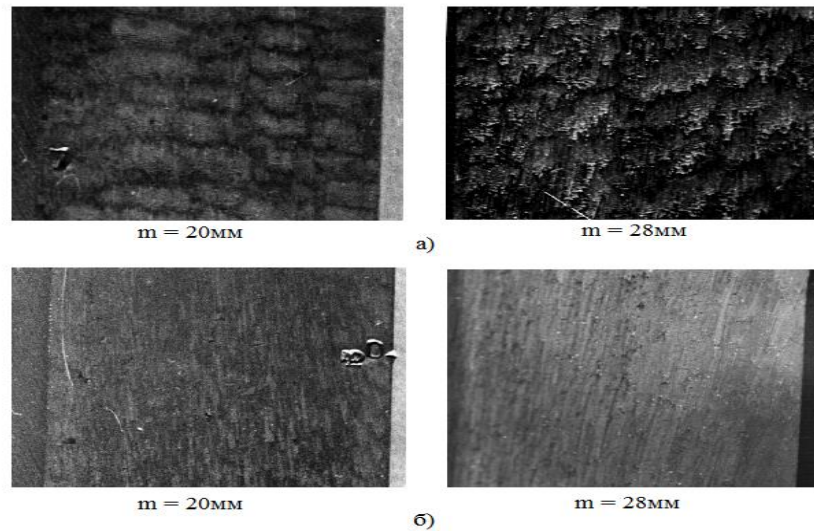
Вид бічної поверхні зубів коліс  $m = 20$  мм й  $m = 28$  мм ( $\Delta = 0,5$ м;  $S = 4$  мм/об;  $V = 1,0$  м/с): а - оброблення стандартною фрезою; б - оброблення фрезою з роздільною схемою формоутворення
